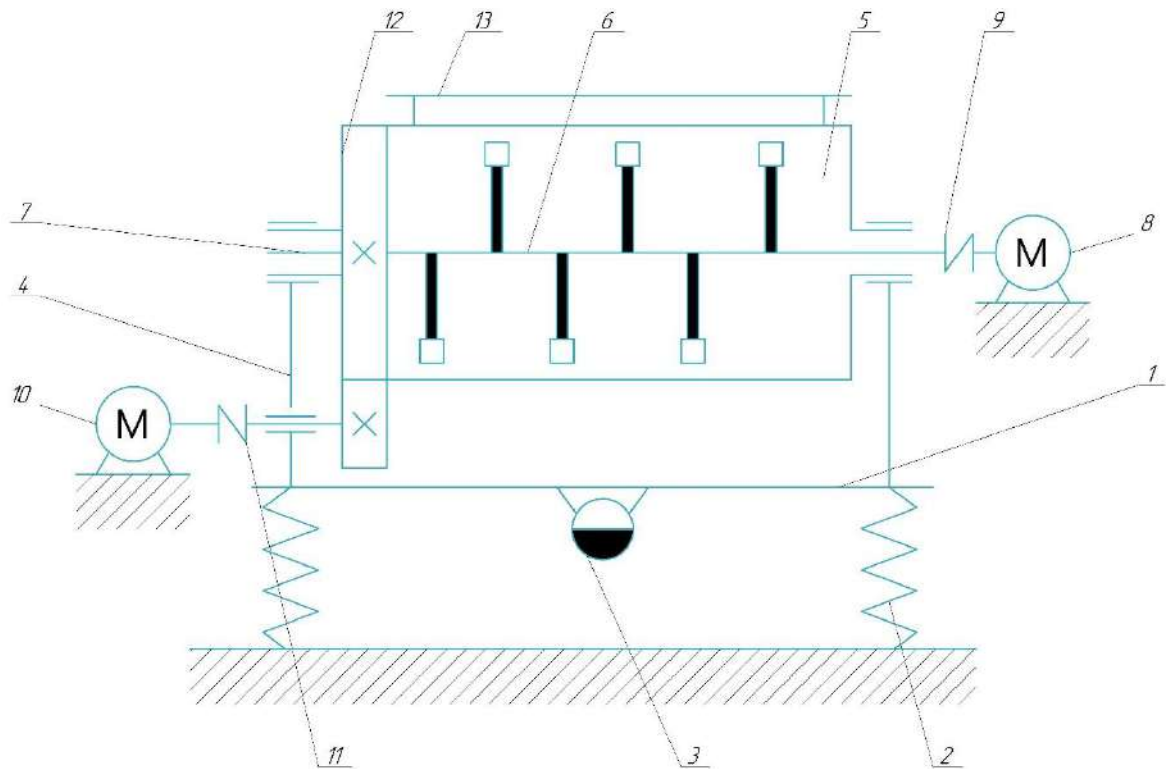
Кінематична схема вібраційного змішувача: 1 – платформа; 2 – елементи пружні; 3 – вібробуджувач; 4 – стійки; 5 – контейнер; 6 – вал лопатевий; 7 – вузол підшипниковий; 8, 10 – електродвигун; 9, 11 – муфта; 12 – передача зубчаста; 13 – люк
